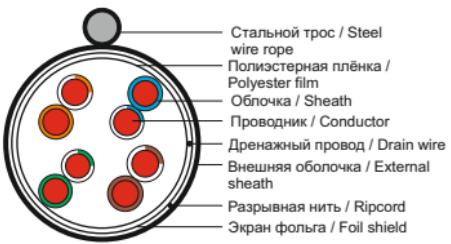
Конструкция кабеля типа F/UTP (со стальным тросом) / Figure 8 – Cable design of F/UTP type (with steel wire rope)
